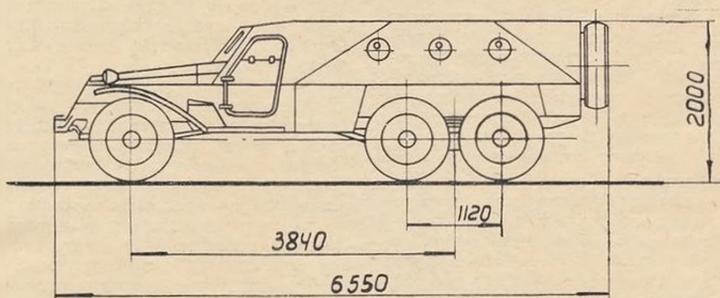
Общий вид и габаритные размеры бронетранспортера БТР-152.
